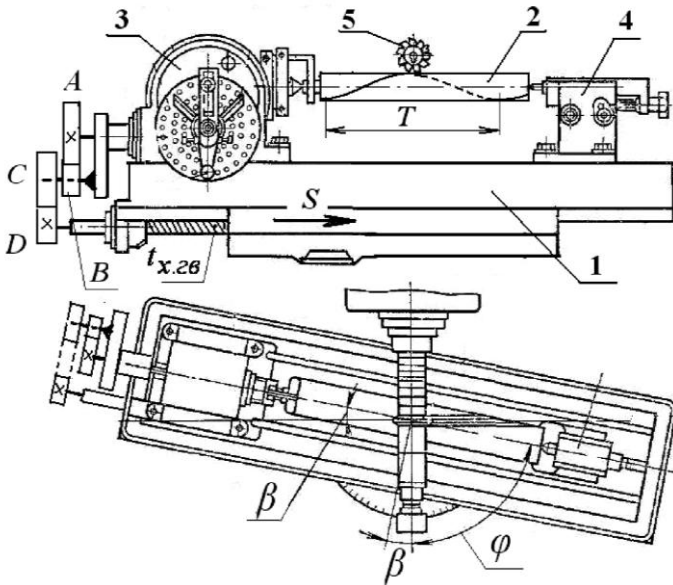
Схема нарізання спіральної канавки за допомогою УДГ на фрезерному верстаті
